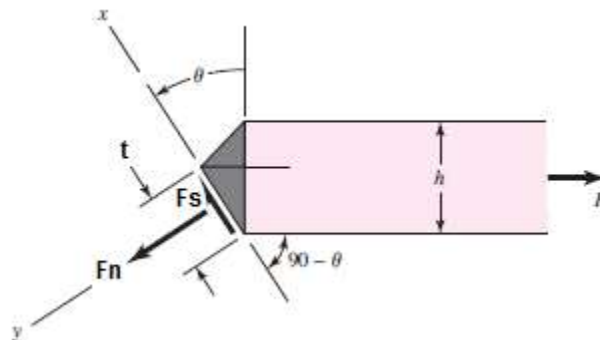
Soldadura de filete dividida. (Budynas & Nisbett)
